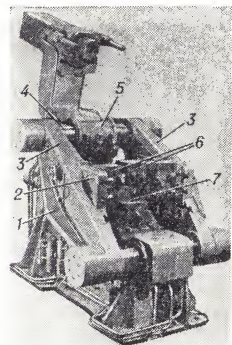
Однопозиционная универсальная кокильная машина (верхняя часть кокиля откинута): 1 — станина; 2 — подвижные плиты; 3 — стойки; 4 — направляющие; 5 — гидравлический цилиндр; 6 — боковые части кокиля; 7 — нижняя плита кокиля.
